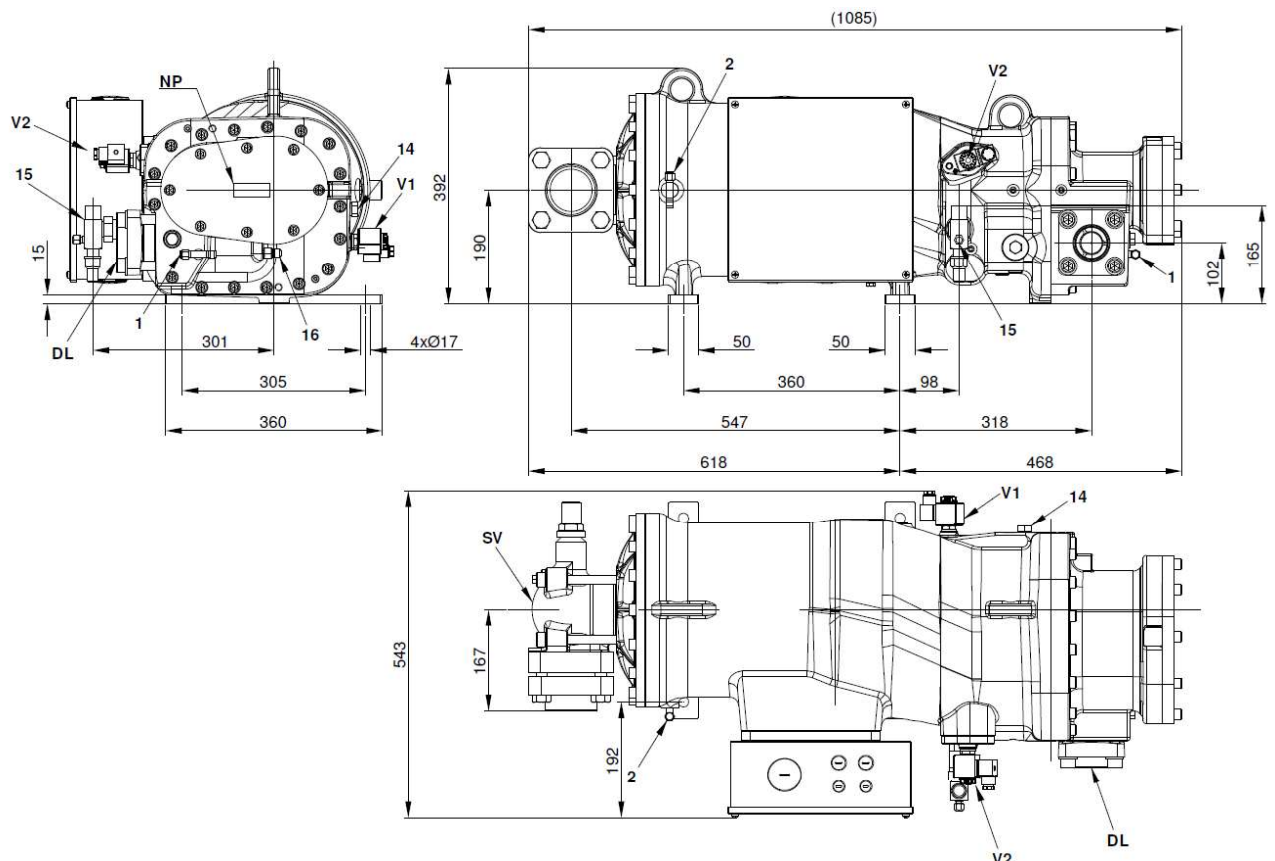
Габаритные размеры винтового компрессора FVR-L-60-200
